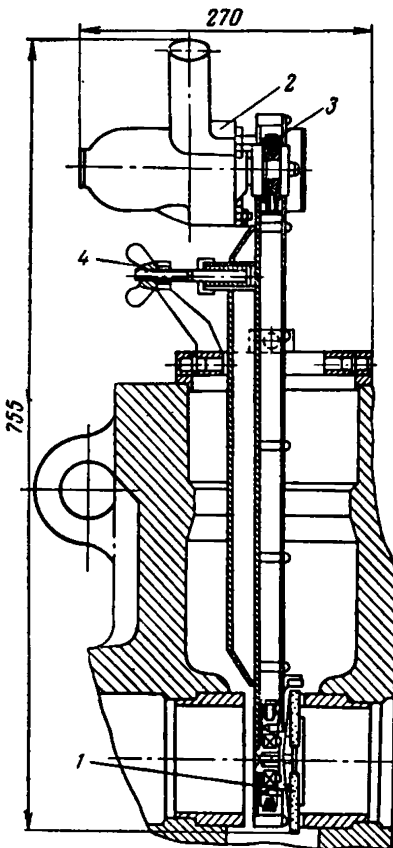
Приспособление для шлифовки седел регулирующих и дроссельных клапанов Ду 100 мм: 1 — шлифовальный круг; 2 — пневмопривод; 3 — клиноременная передача; 4 — гайка
